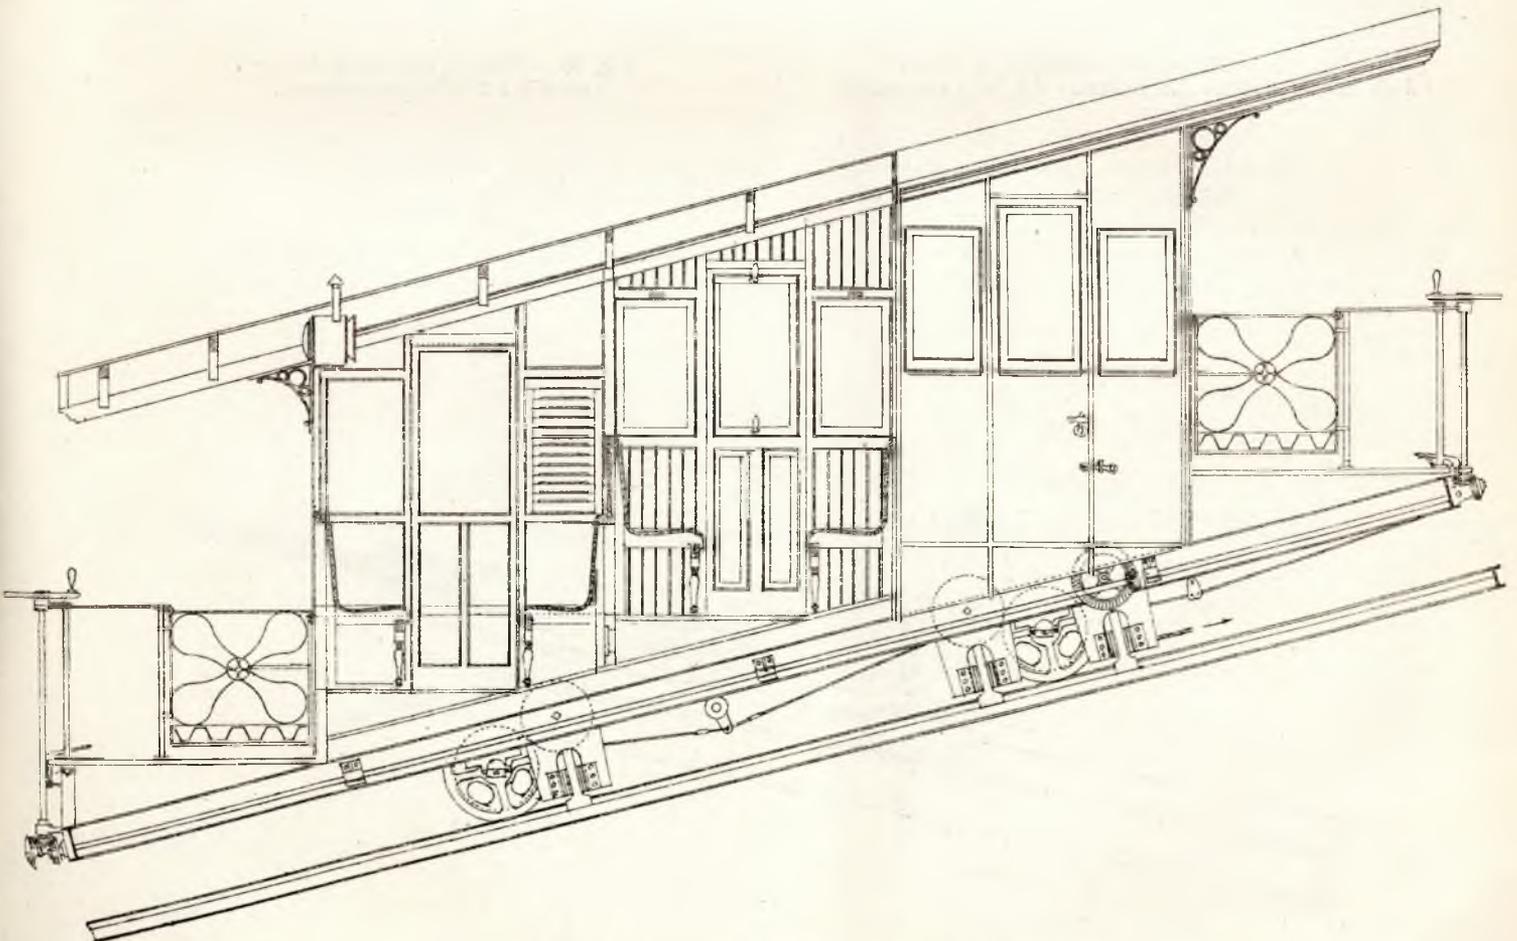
Sezione longitudinale e prospetto laterale di una vettura.
